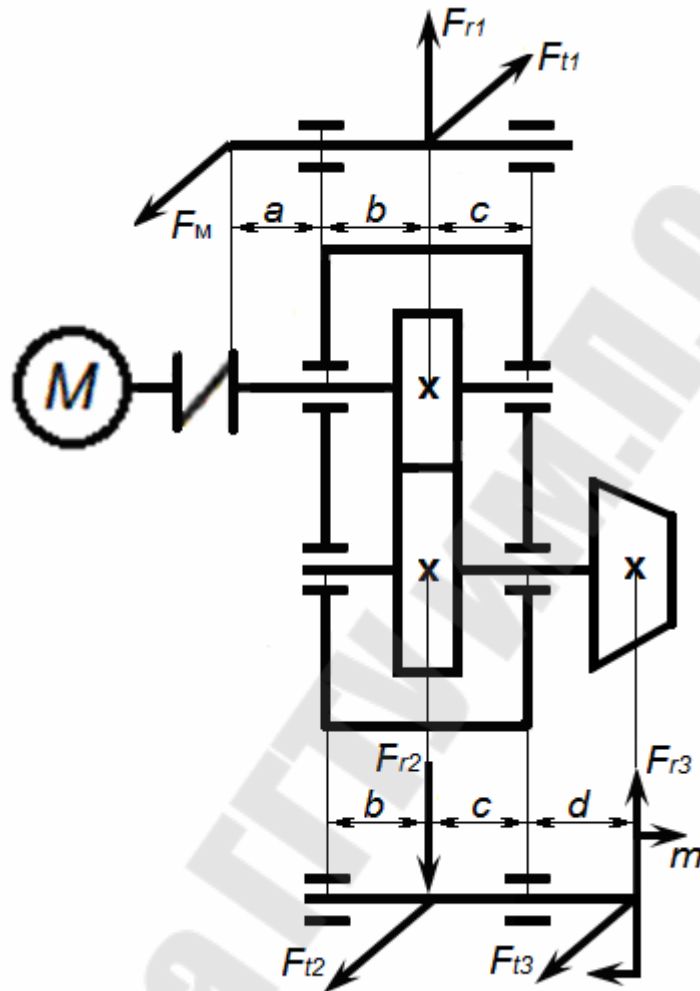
Привод конвейера с открытой конической зубчатой передачей
